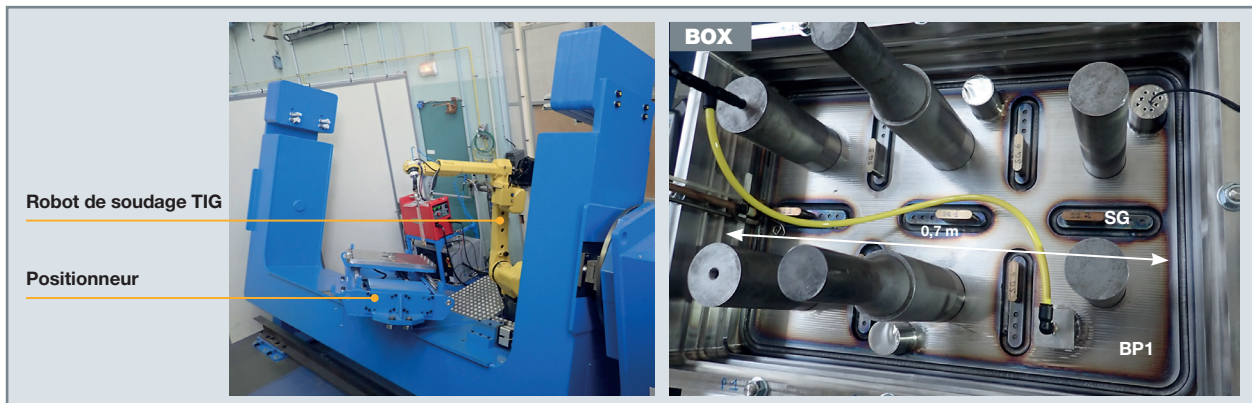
(a) Installation robotisée de soudage TIG, (b) maquette prototype (assemblage des SG et BP1 avec la Box).
